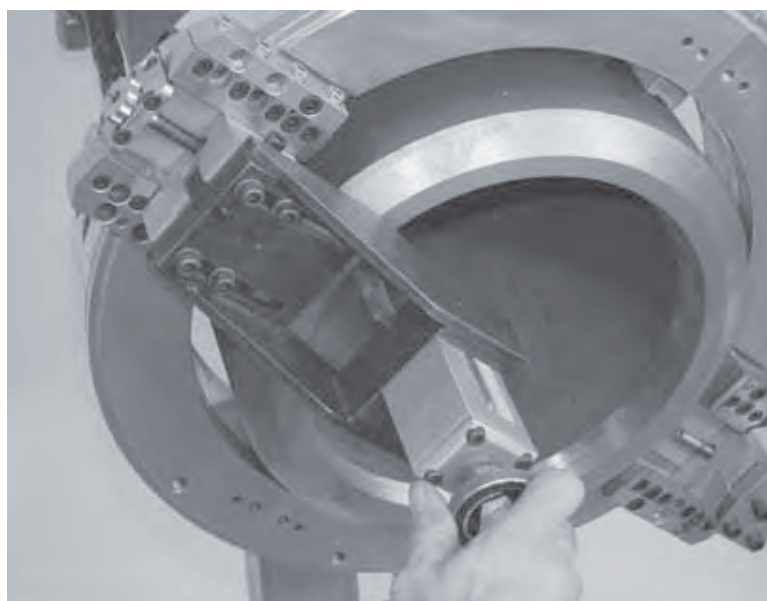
Поворачивайте рукоятку подачи против часовой стрелки
